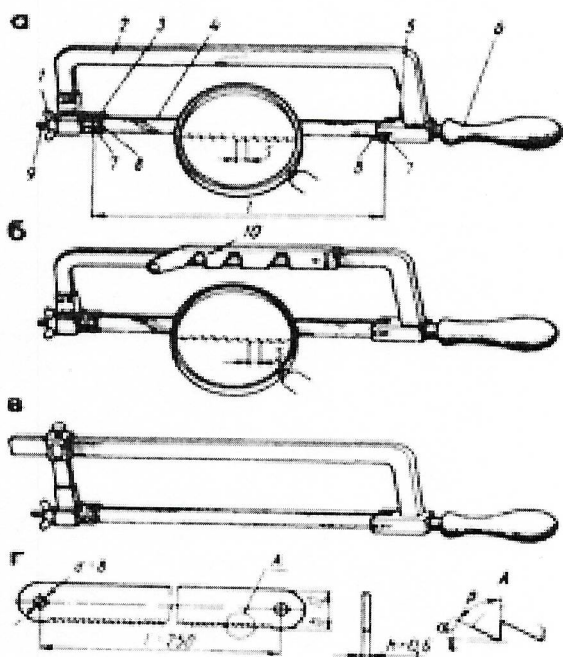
Ручная слесарная ножовка цельная (а), раздвижная (б), с передвижным держателем (в) и ножовочное полотно (г):
